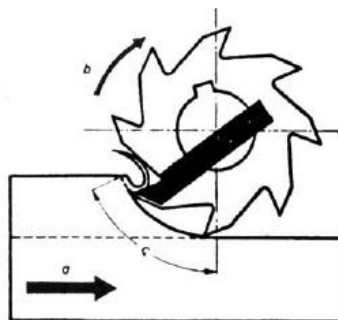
Operação de fresagem: a) movimento de avanço; b) movimento principal ou de corte; c) curso útil de uma navalha [23].
